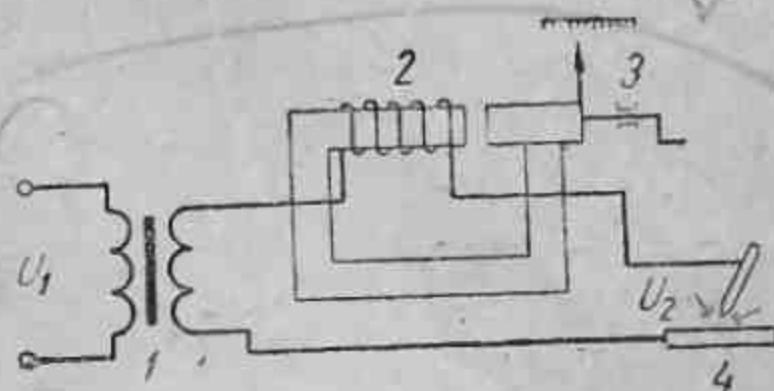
Схема сварочного трансформатора с отдельным дросселем: 1 — сварочный трансформатор; 2 — дроссель; 3 — винт для перемещения ярма; 4 — свариваемая деталь.
